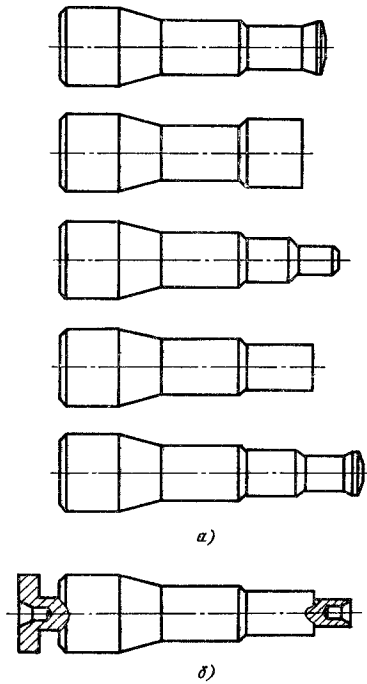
Конструкция пуансонов для холодного выдавливания (а) и эскиз типовой заготовки пуансона с ложными центрами (б)
